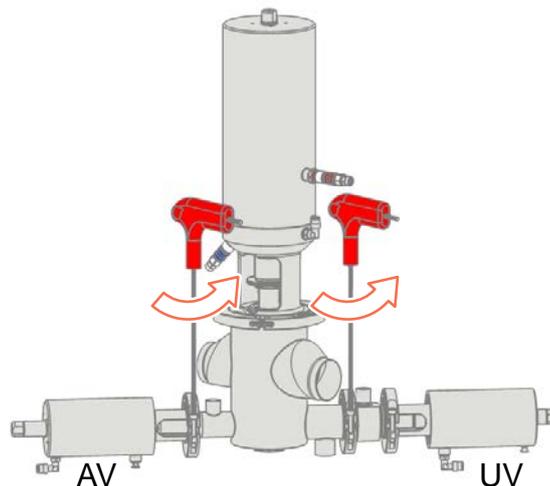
Débloquer la vis du collier de serrage de la vanne latérale
